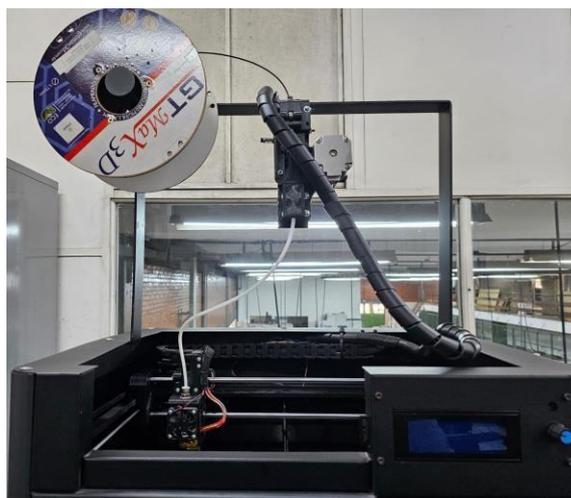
Primeira estrutura construída e já fixada em seu lugar determinado com realocação da fiação elétrica.
